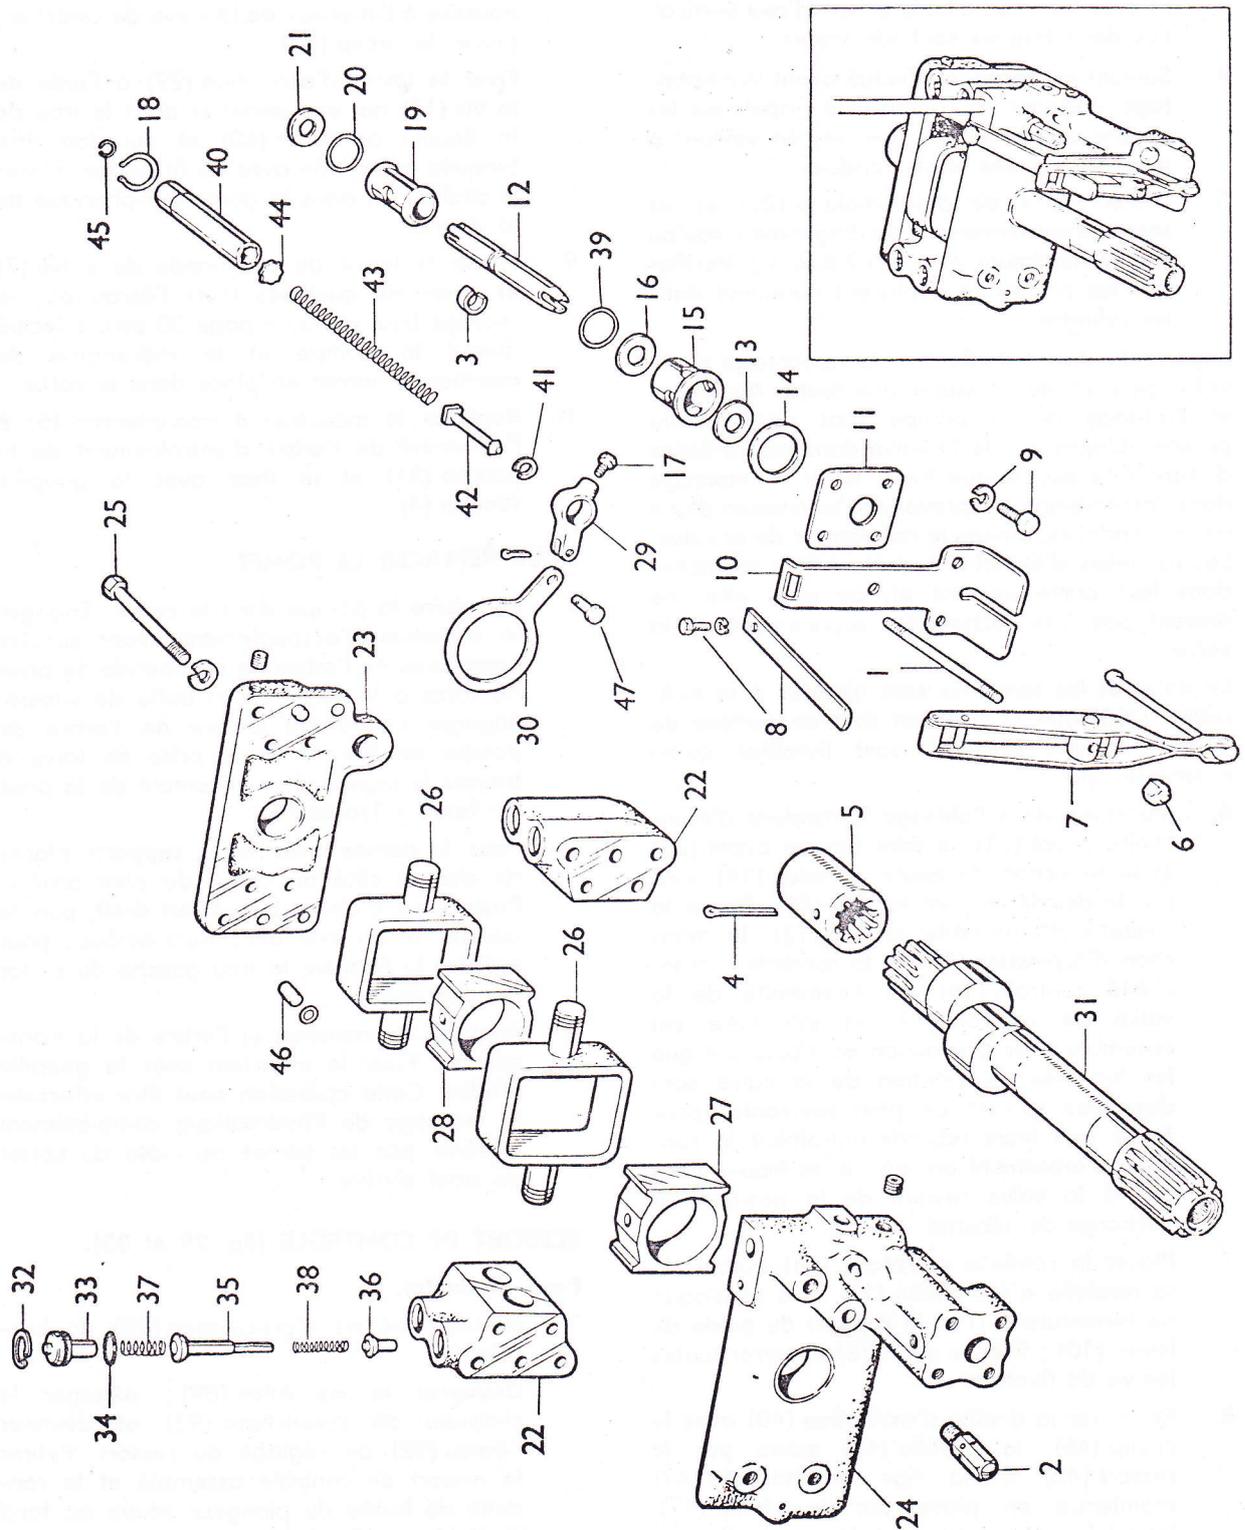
VUE ÉCLATÉE DE LA POMPE HYDRAULIQUE.
